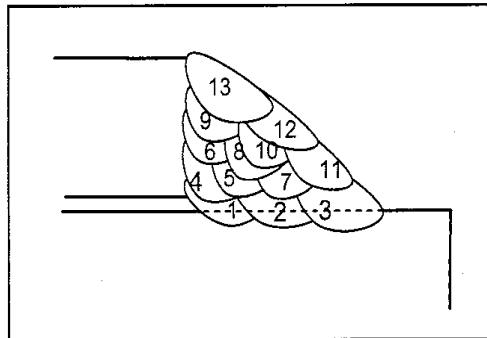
Localização de passes na soldadura longitudinal
